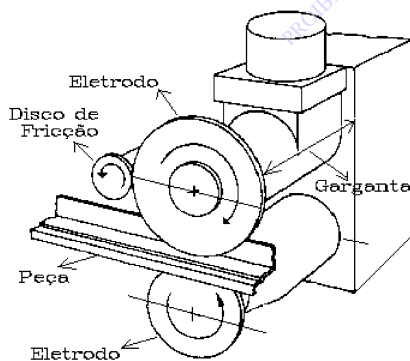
(a) - Equipamento básico para Soldagem por Costura.
